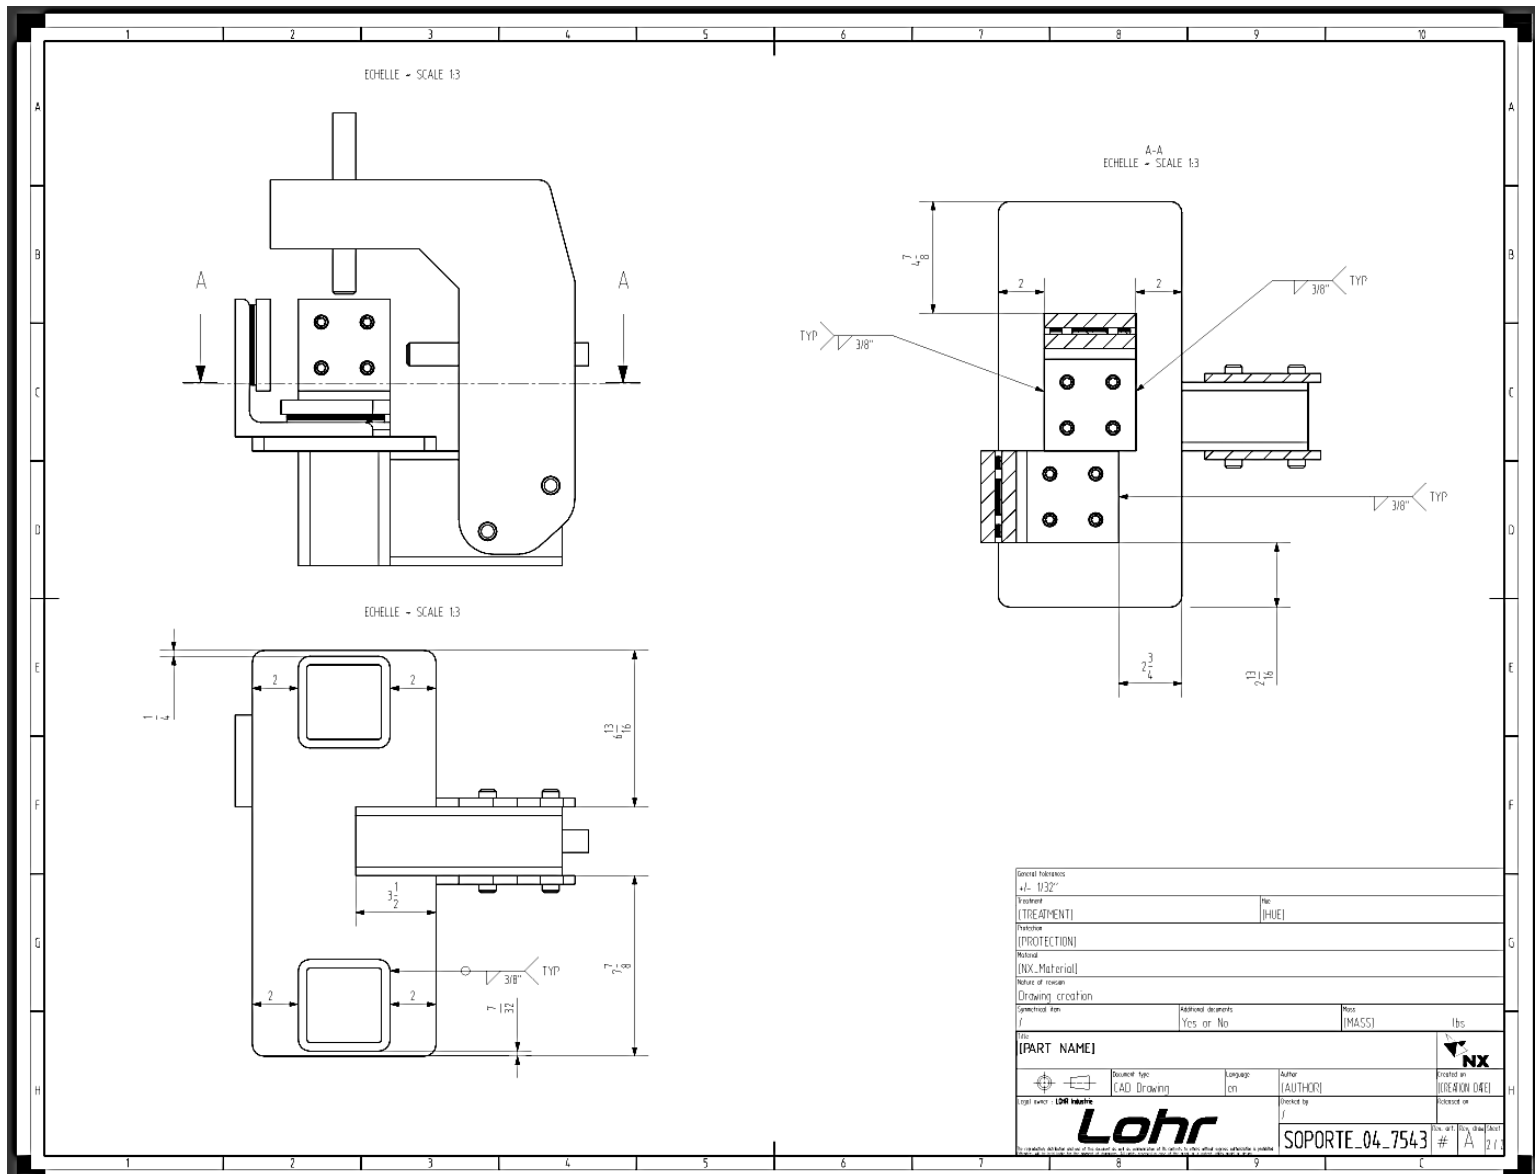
Ejemplo de plano (dimensiones y soldadura) .
